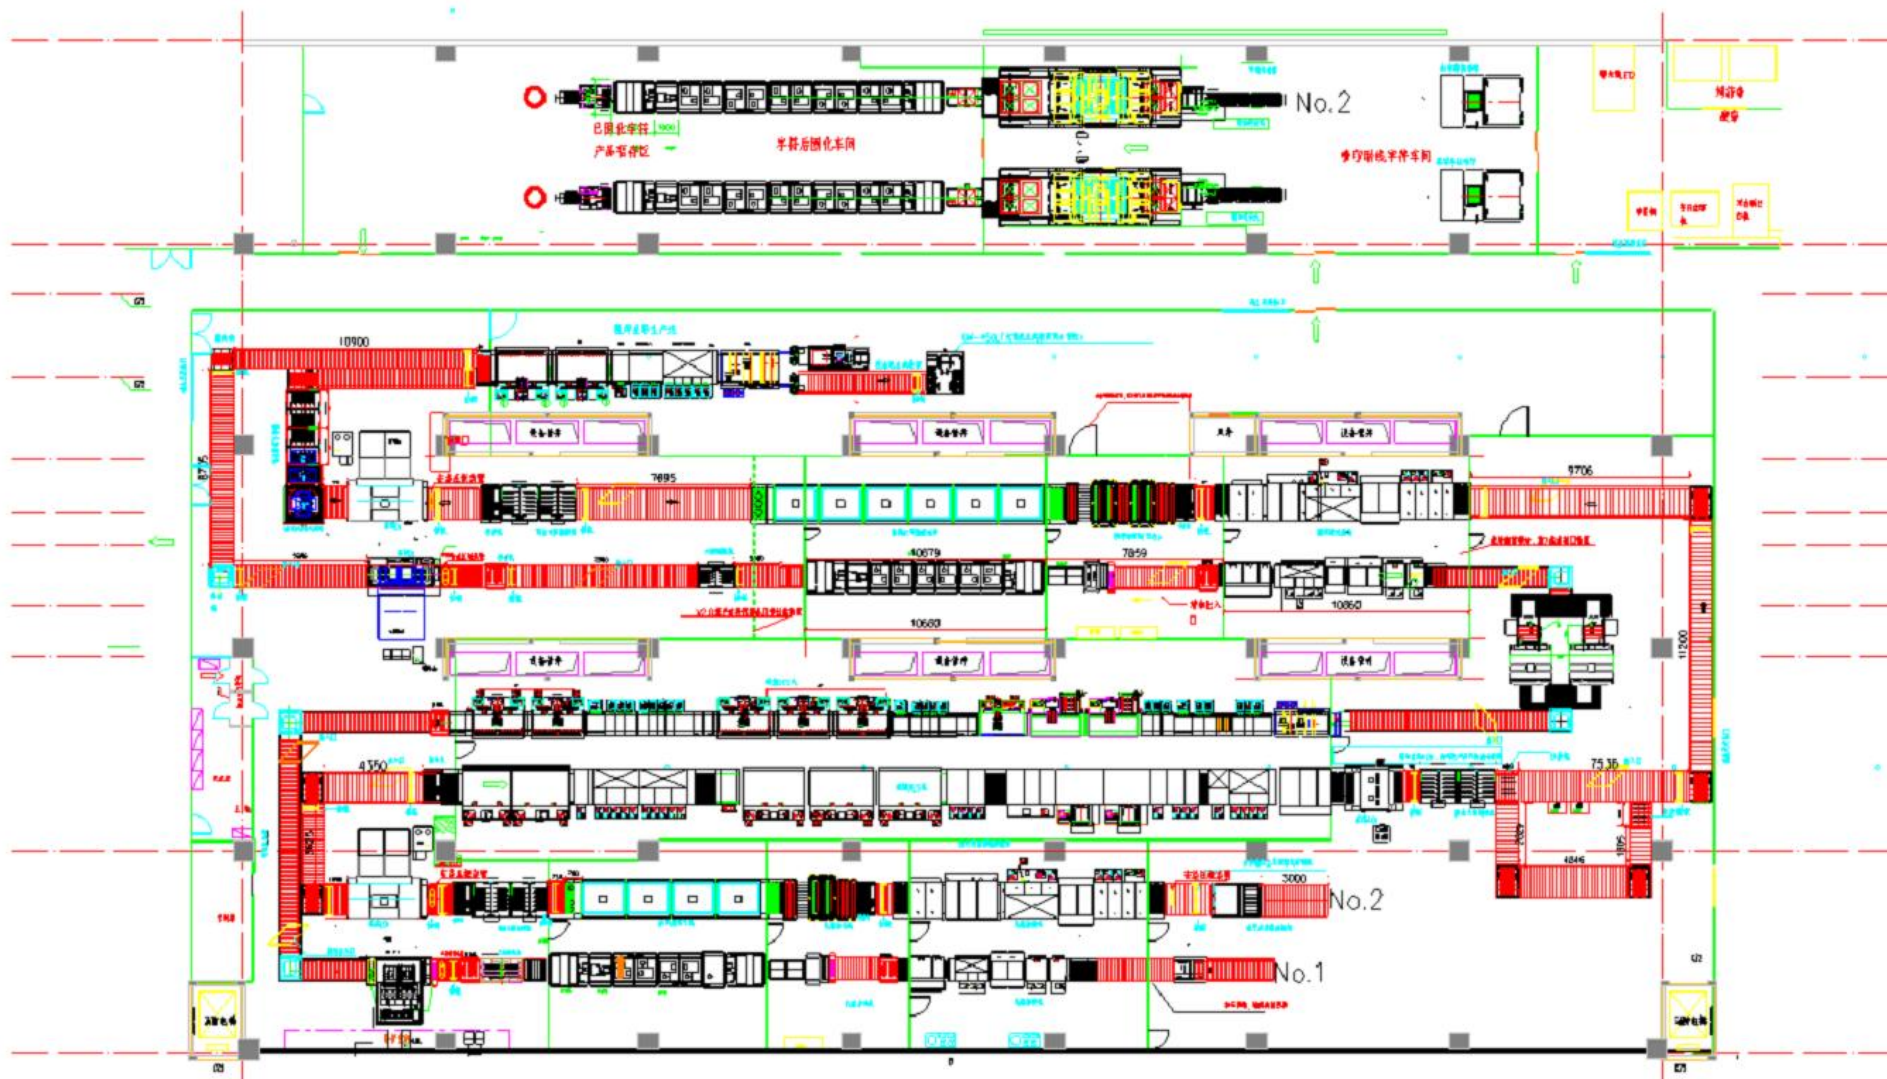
本项目二号厂房 6 楼实际平面布置图
